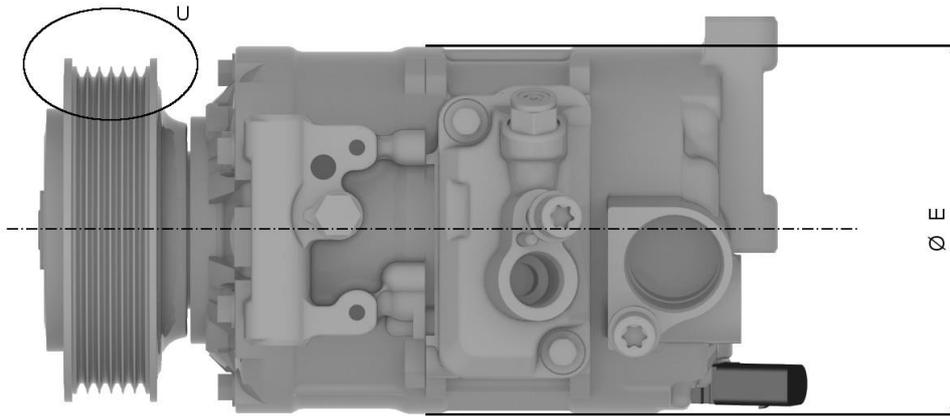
Dimensions du compresseur de fluide frigorigène, vue de dessus (exemple DENSO-7SEU17)
